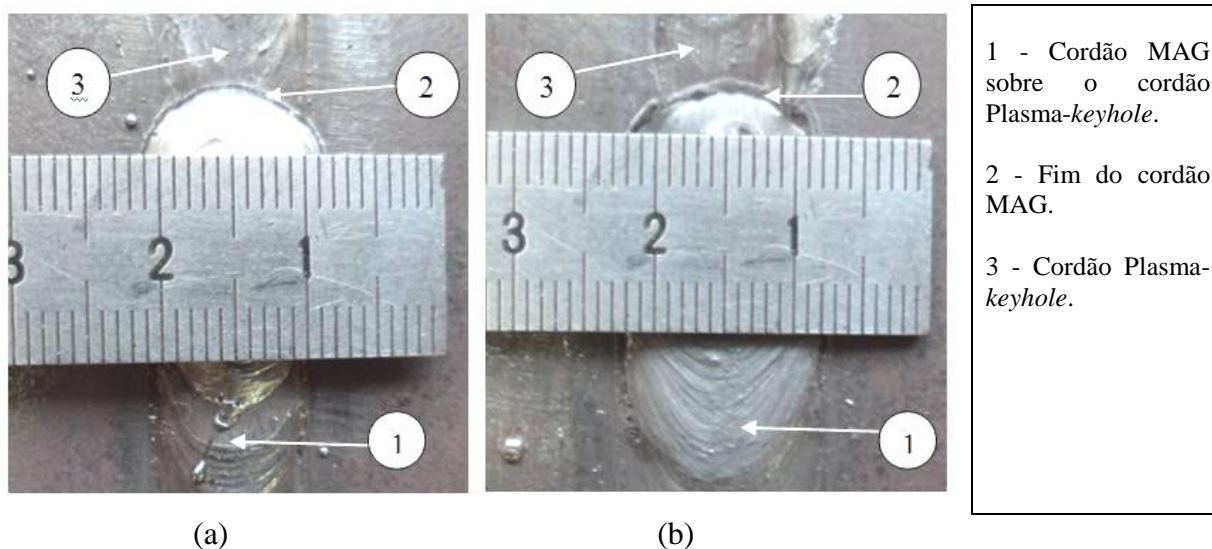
Aspecto do cordão de solda produzido pelo processo MAG. (a) sem pré-aquecimento e; (b) com pré-aquecimento
